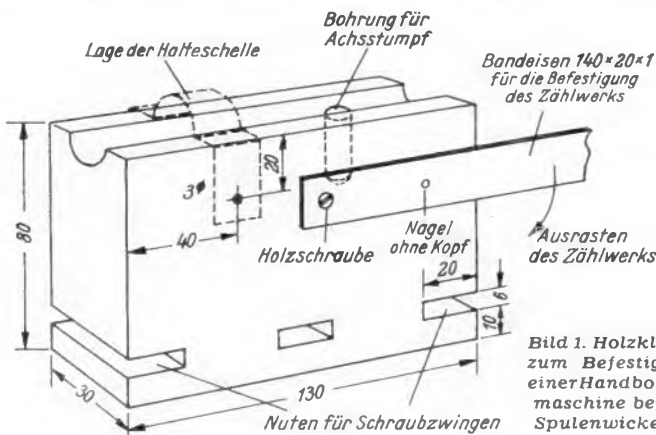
Holzklötzchen zur Befestigung einer Handbohrmaschine beim Spulwickeln
